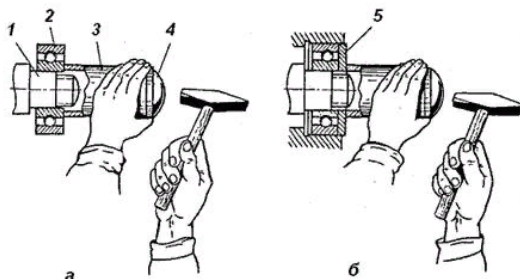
Насадка подшипников качения: а – на вал; б – на вал и в расточку подшипникового щита
